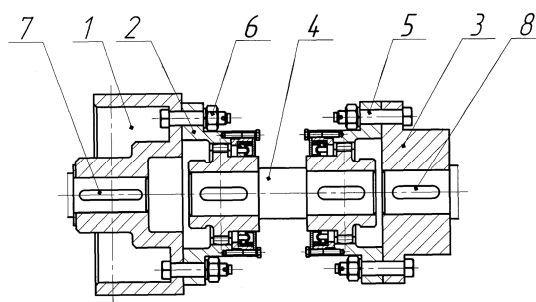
Эскиз промежуточного вала: 1 – шкив; 2 – зубчатая полумуфта; 3 – полумуфта; 4 – вал; 5 – крепёжное соединение; 6 – крепёжное соединение; 7 – шпонка; 8 – шпонка
